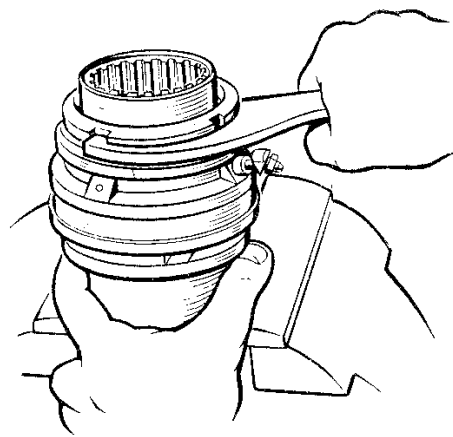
Отвертывание гайки крепления подшипника промежуточной опоры
